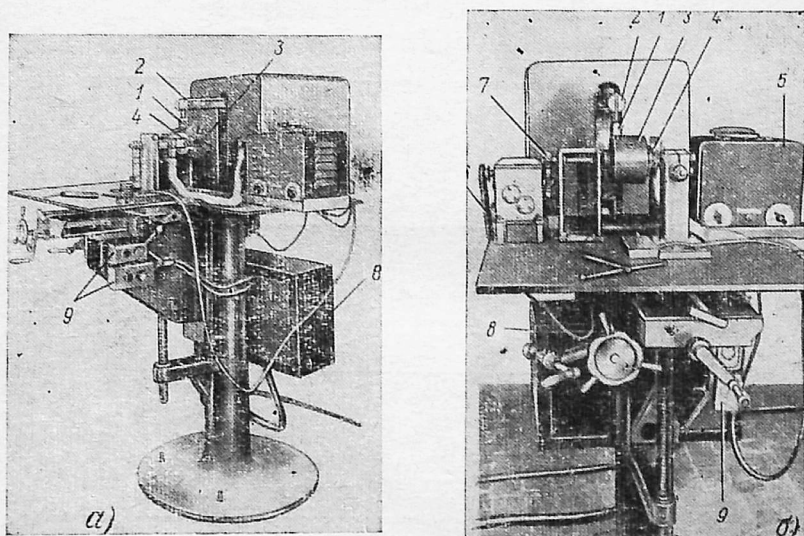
Станок для игнитронной контактной роликовой сварки с машиной ОУ-56 и прерывателем УИП-1.
